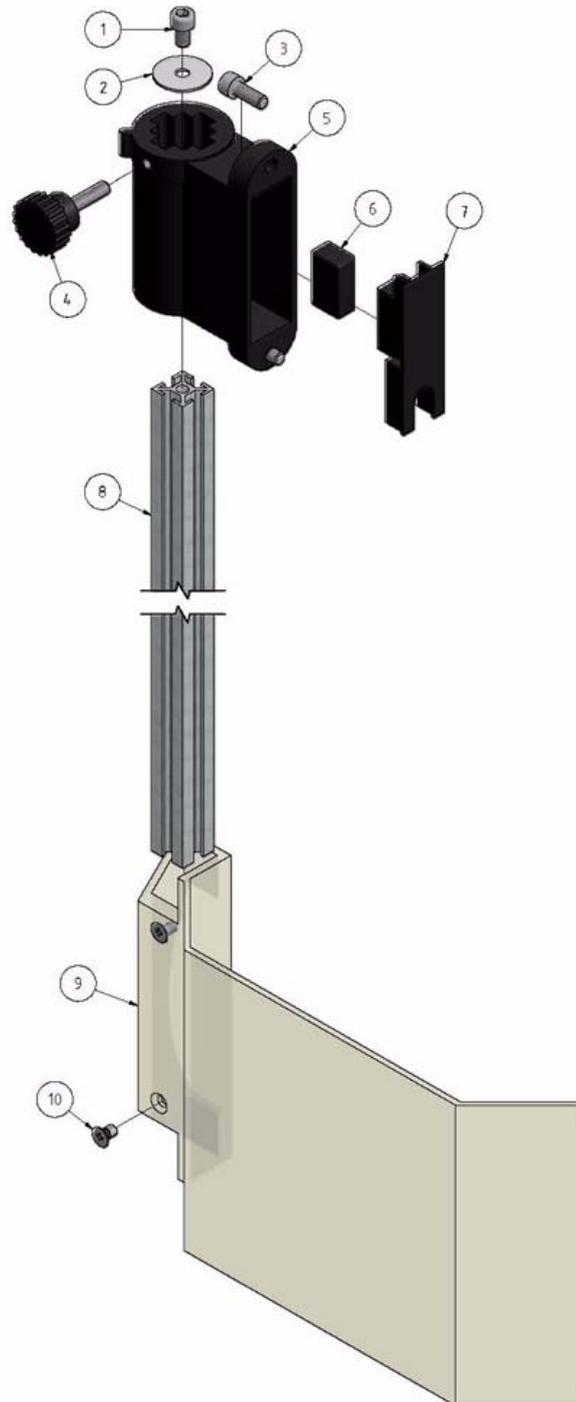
Bohrfutterschutz - Drilling chuck protection
